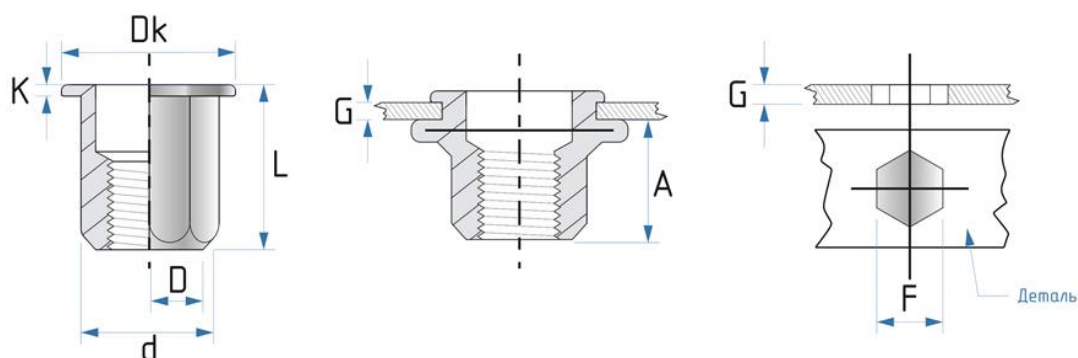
Заклёпка резьбовая шестигранная, стандартный борт
